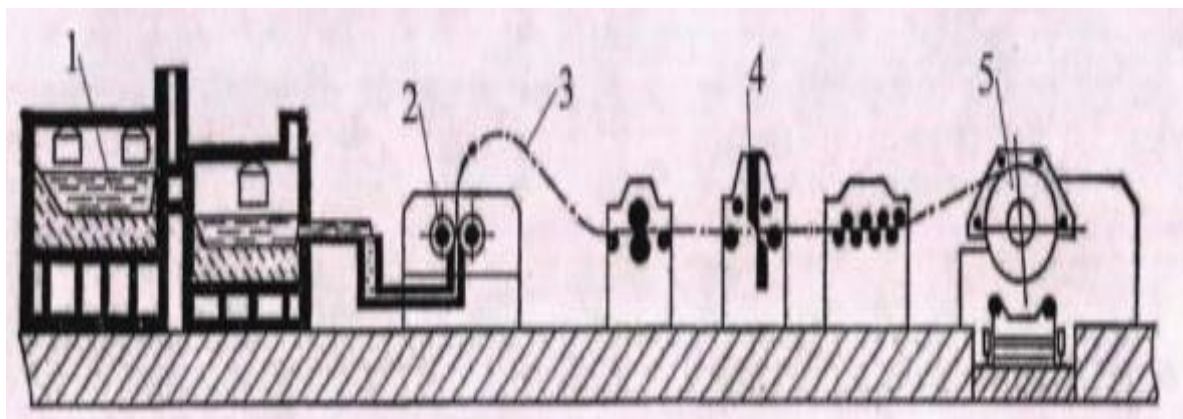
Схема установки для литья алюминиевых сплавов в двухвалковых агрегатах при подаче металла снизу
